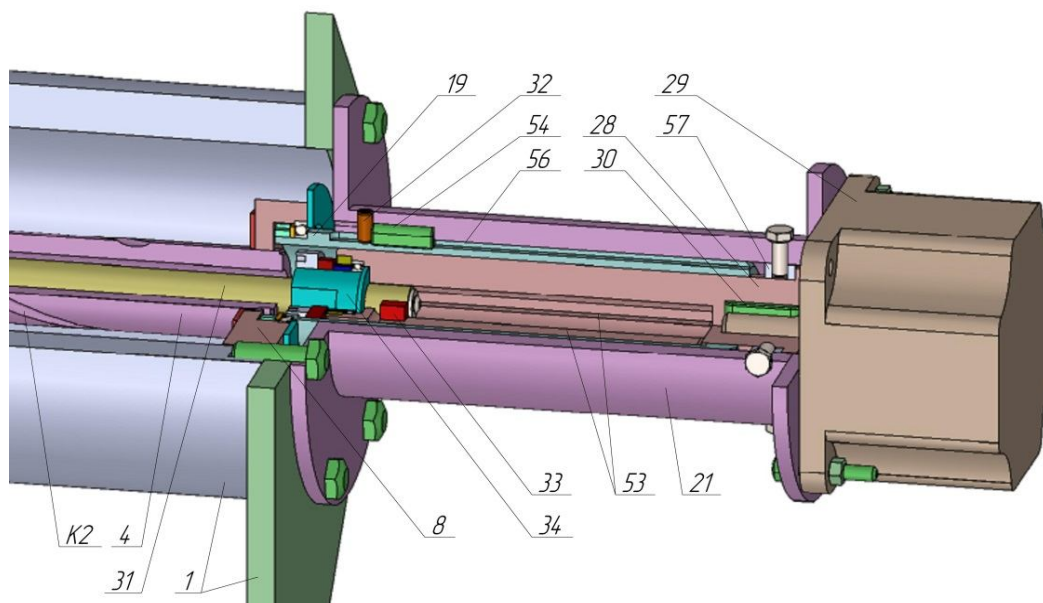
Конструктивне рішення передачі гвинт–гайка механізму регулювання положення рухомих дебалансів
